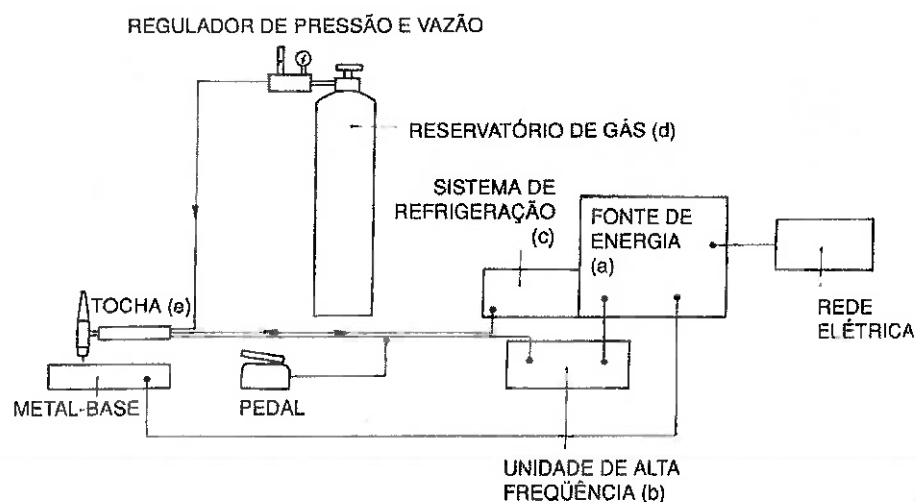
Esquema dos equipamentos necessário para a soldagem GTAW
